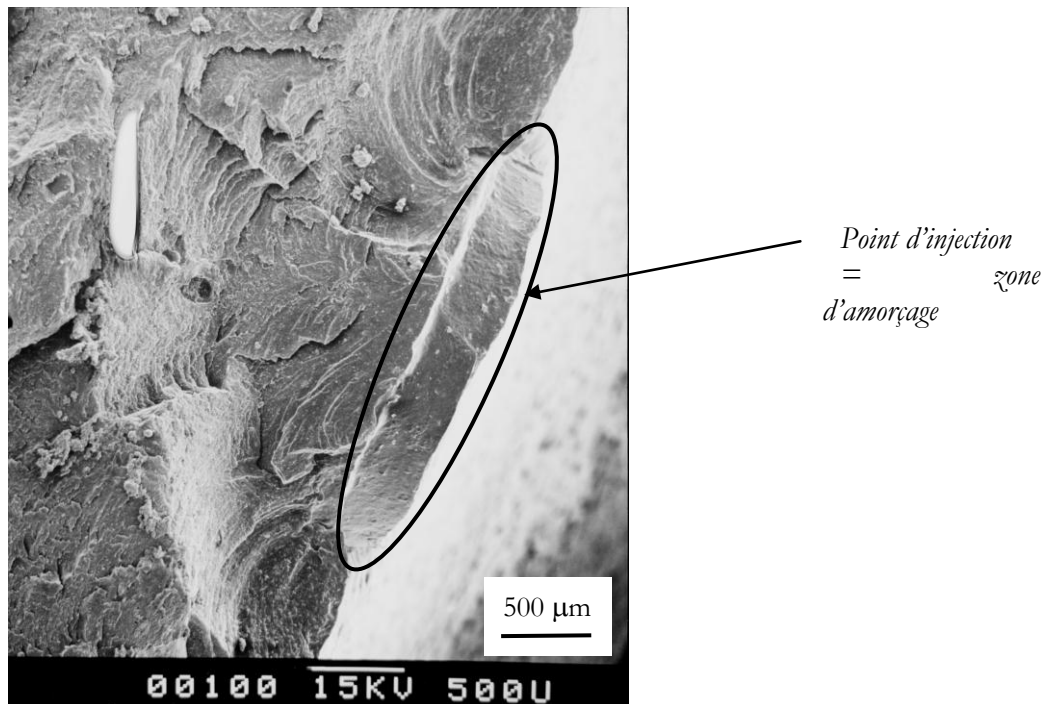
Essai AP1 – Amorçage sur le point d'injection
